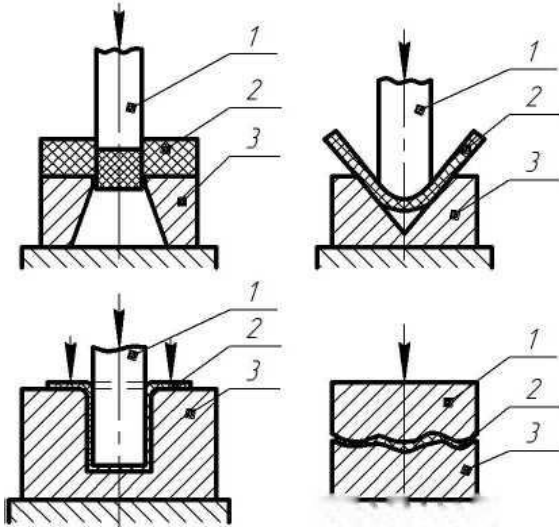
Етапи листового штампування: 1 – пуансон; 2 – заготовка; 3 – матриця
